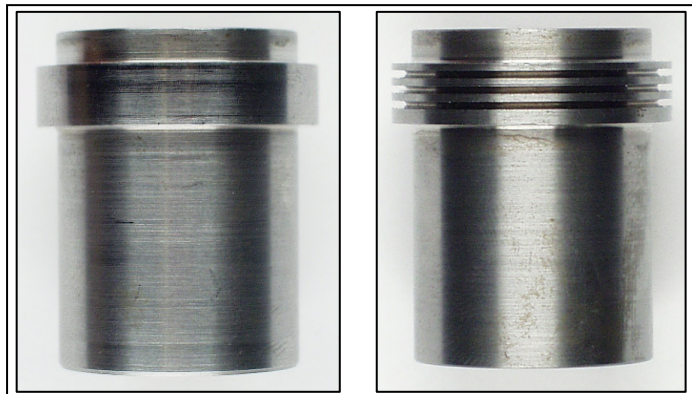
Probekörper mit glatter Dichtfläche bzw. mit Labyrinthdichtung
